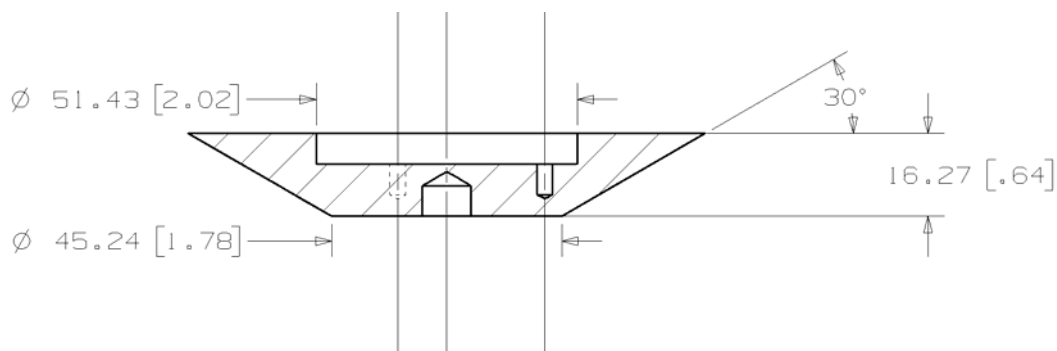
Parte dinámica del cojinete neumático. Dimensiones en mm [plg].
